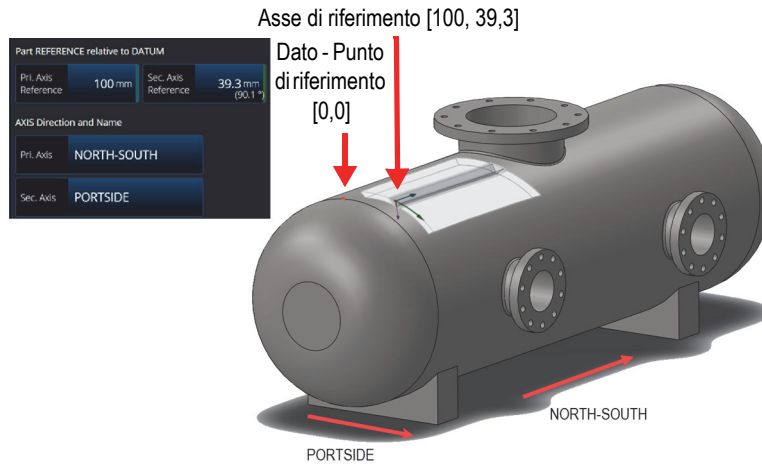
Scan Plan &gt; Part &amp; Weld &gt; Substep 2 (sottofase 2)
